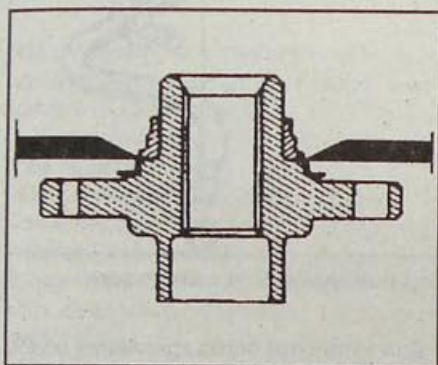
Установка захватов съемника для снятия внутреннего кольца подшипника со ступицы переднего колеса
